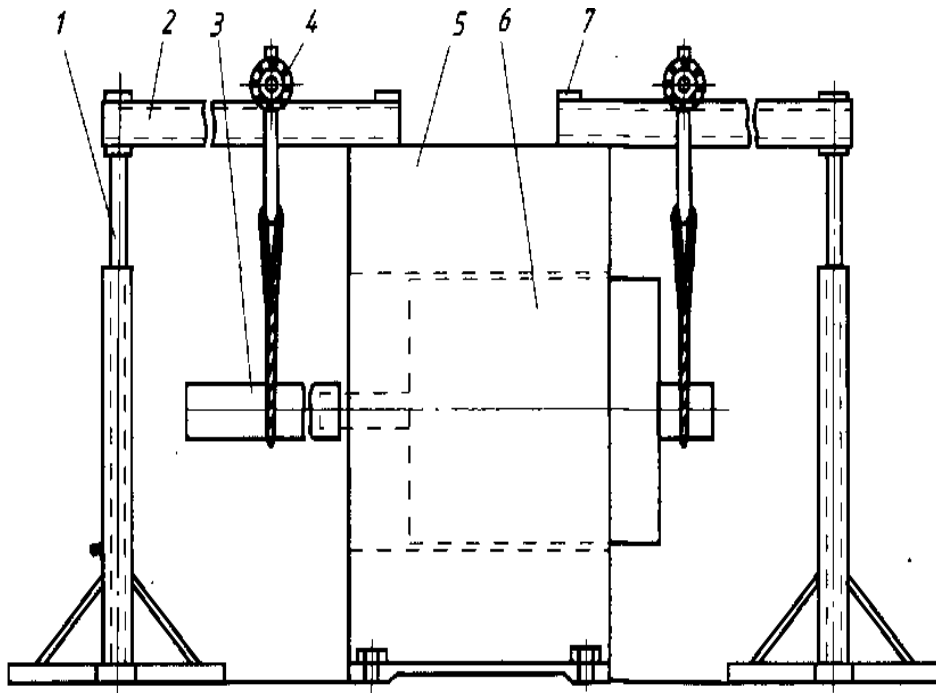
Схема ввода ротора в статор с применением удлинителя и специального приспособления:
